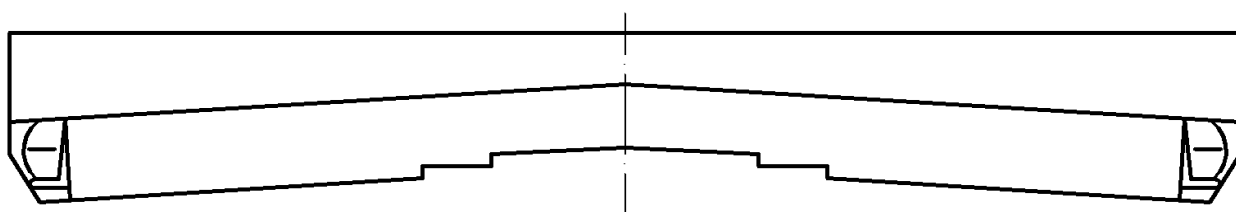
Шевронный нож со сложной формой режущей кромки конструкции «НКМЗ» [80]
